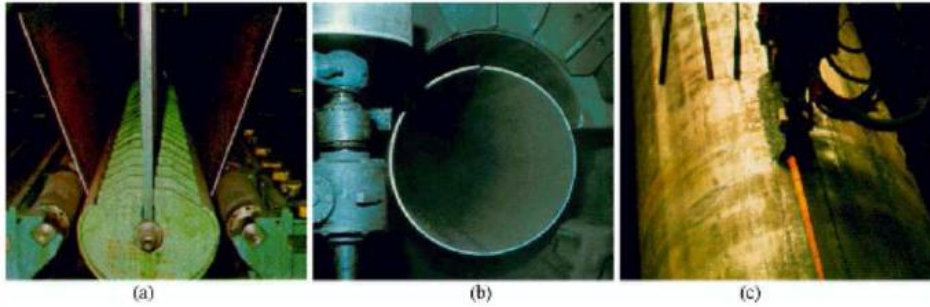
Formage en U (a), formage en O (b) et soudage (c) de la fabrication des tubes soudés en long
